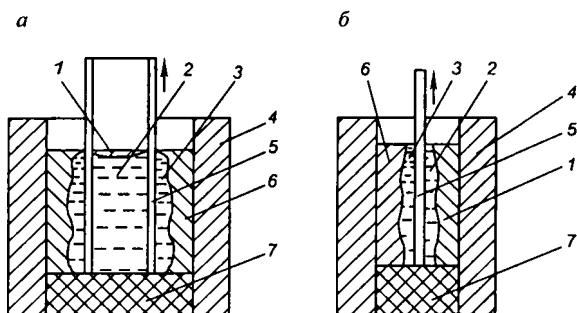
Схемы получения биметаллических заготовок в кокилях:
